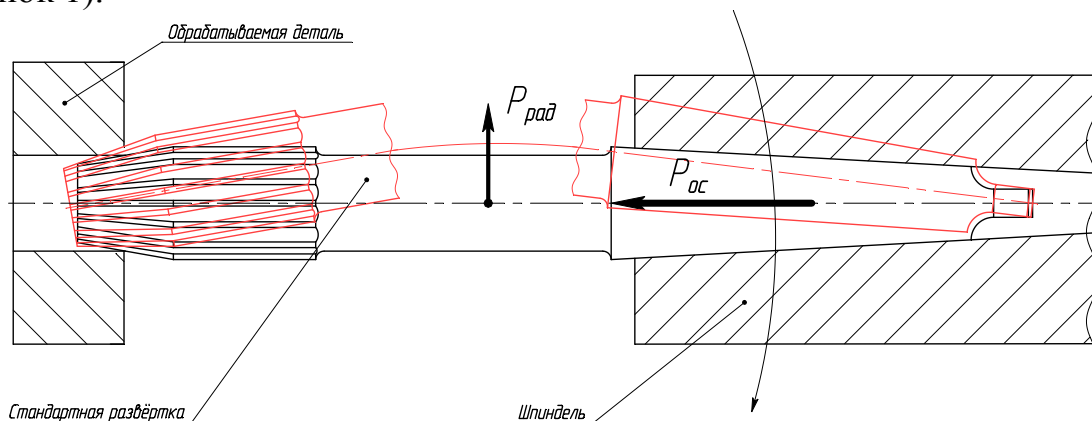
Схема обработки отверстия стандартной развёрткой
